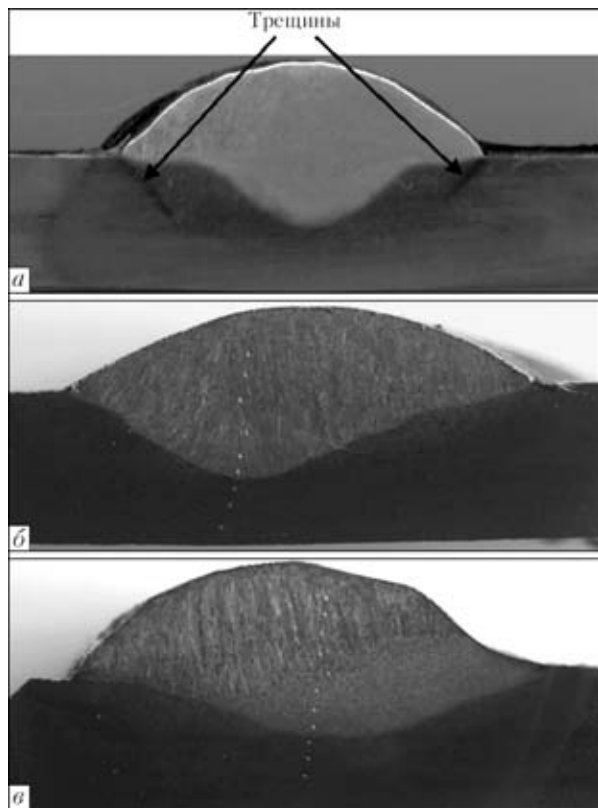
Макрошлифы поперечных сечений валиков при различных условиях наплавки: а — без предварительного подогрева; б — с предварительным подогревом; в — последовательная наплавка двух валиков
